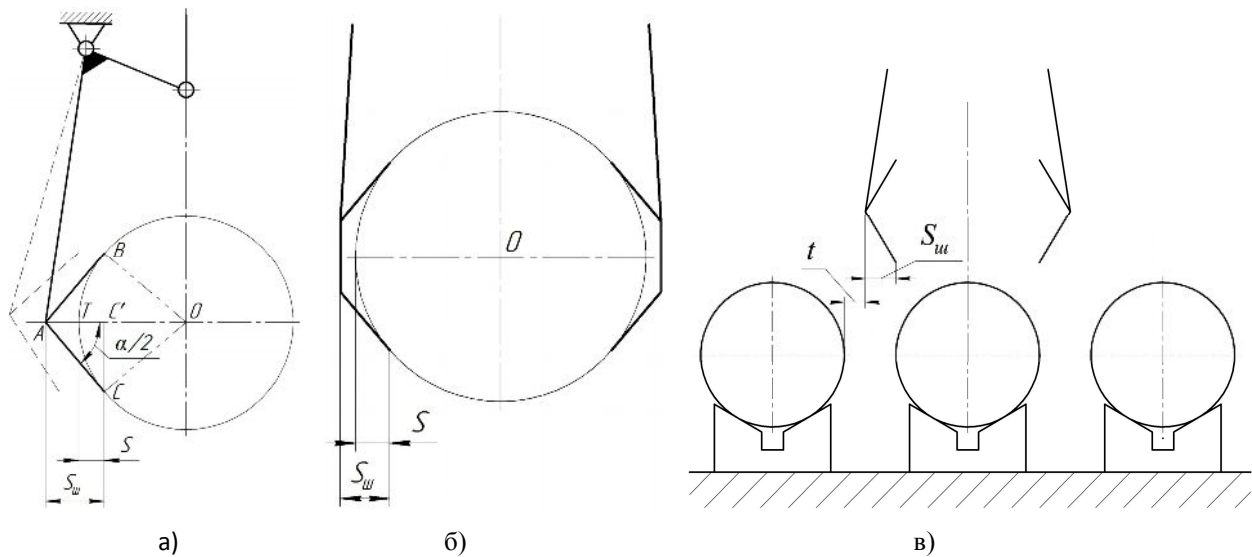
Розрахункові схеми умов захоплення деталі
